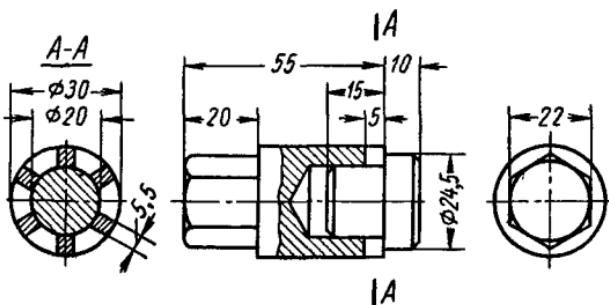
Ключ для затяжки гаек крепления стаканов форсунок
